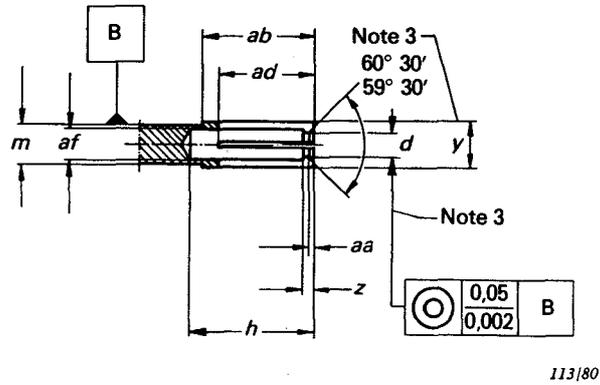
B. — Dimensions du contact central femelle (voir le tableau).
